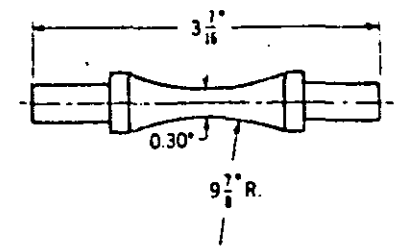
Probeta para la máquina de ensayos de viga rotatoria de R.R. Moore.
